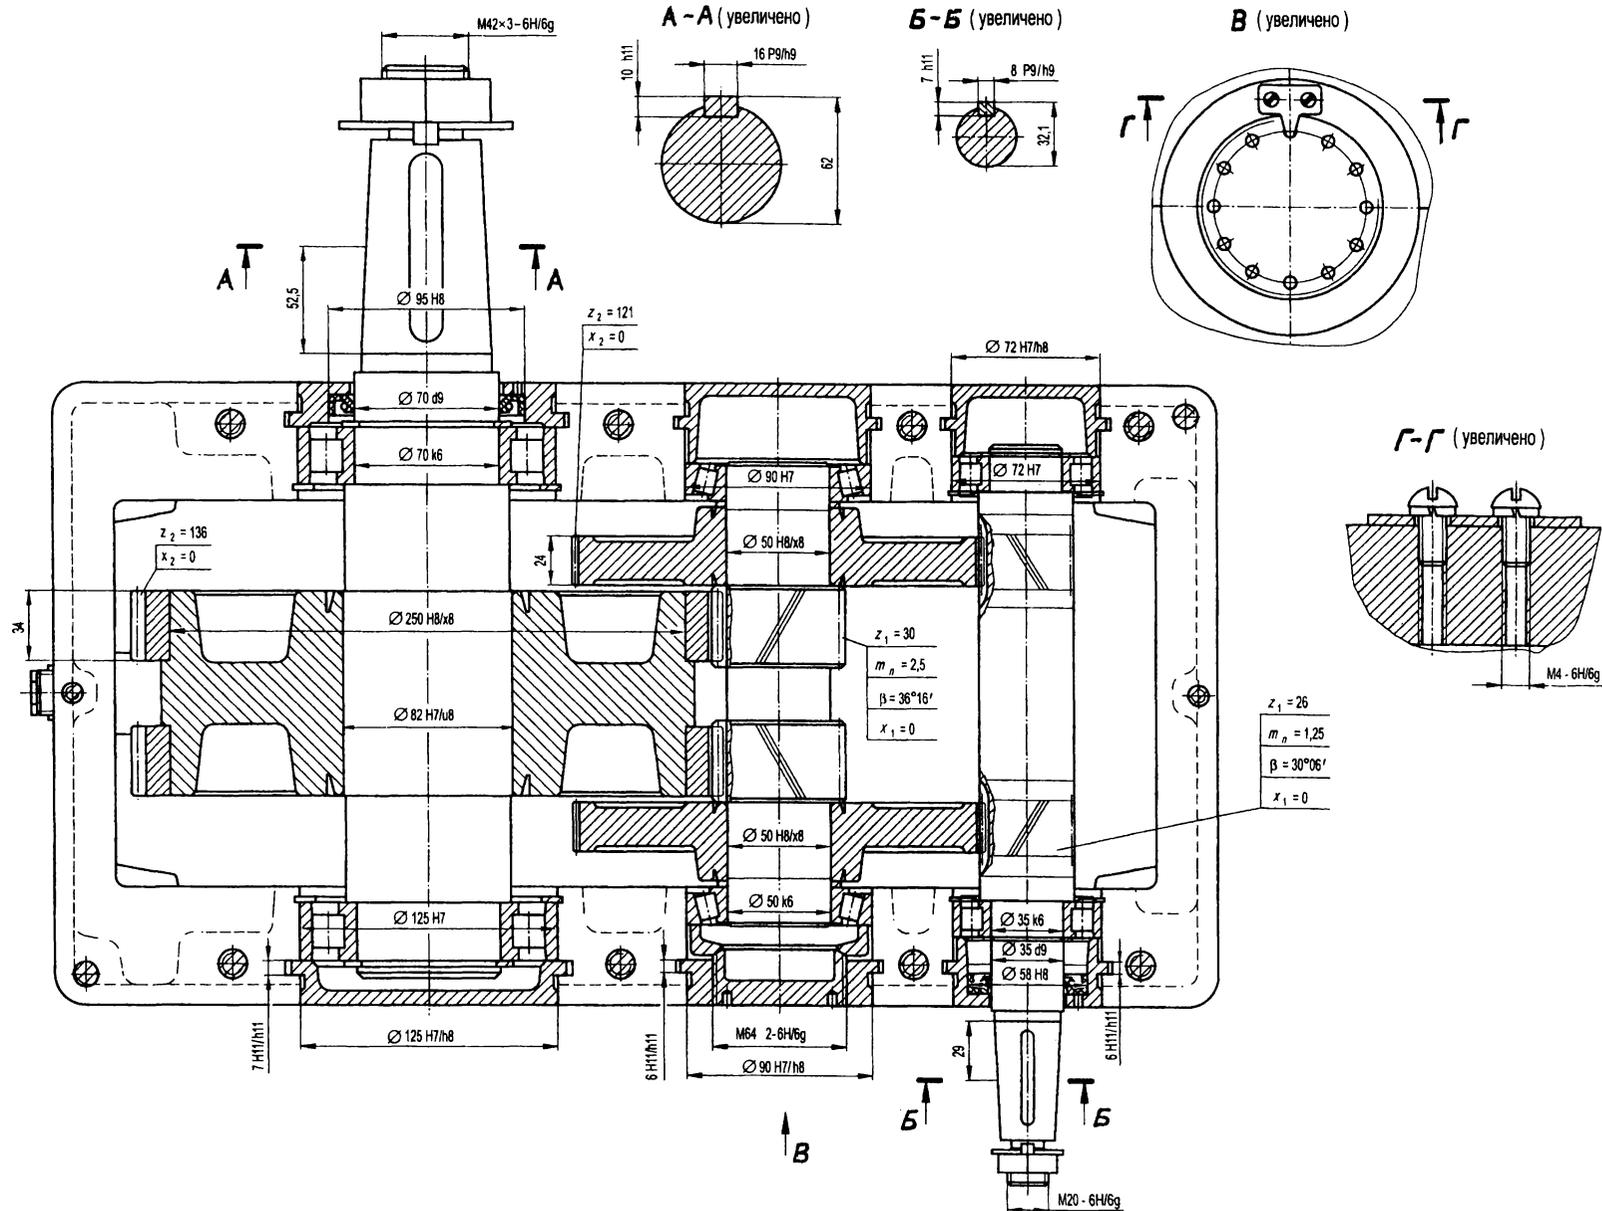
Редуктор двухступенчатый цилиндрический горизонтальный с шевронными передачами
